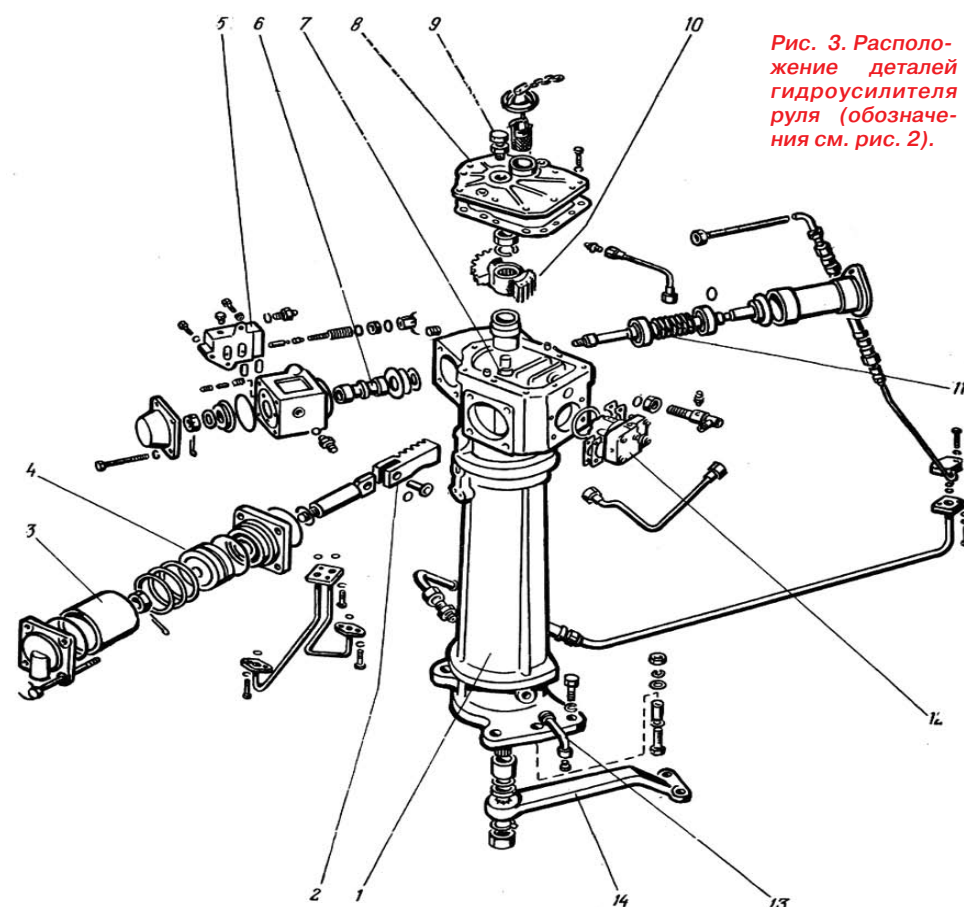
Расположение деталей гидроусилителя руля (обозначения см. рис. 2).
